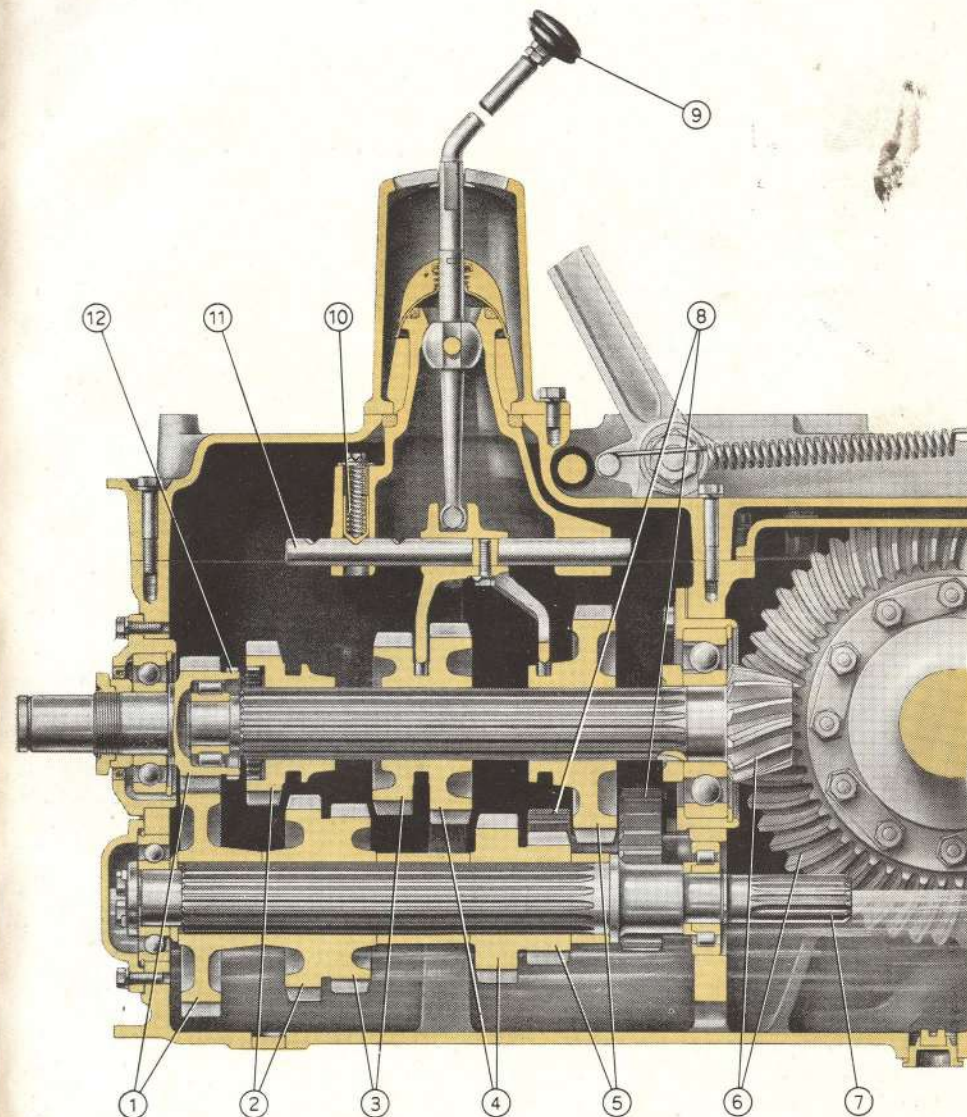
Coupe longitudinale sur les pignons de la boîte de vitesses.
